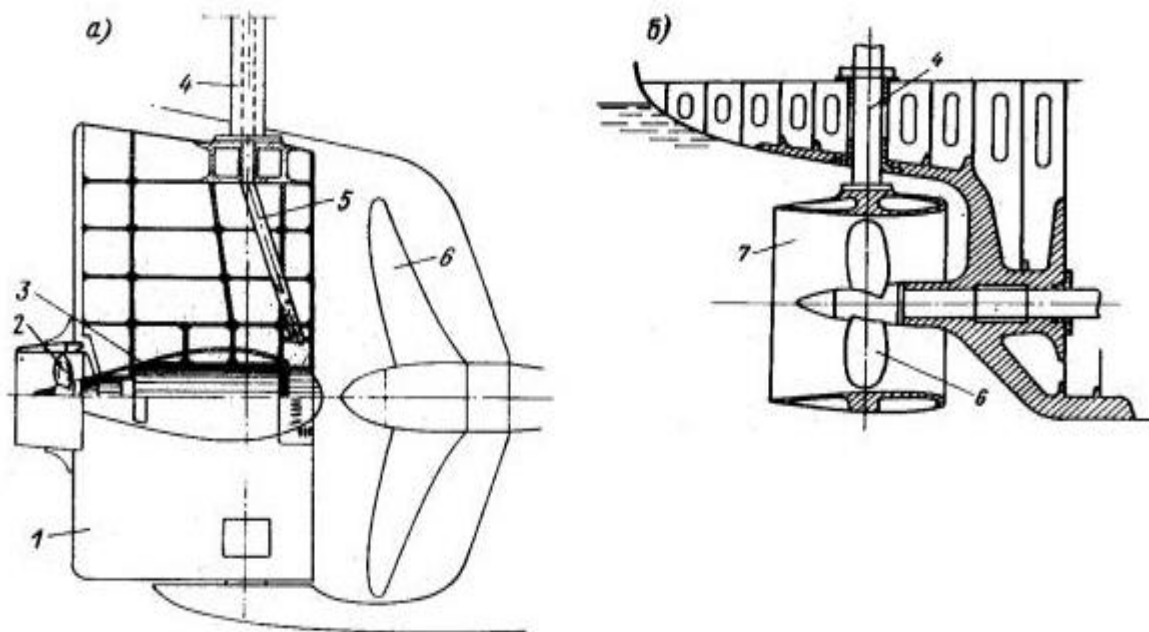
Активный руль (а) и поворотная насадка (б):
